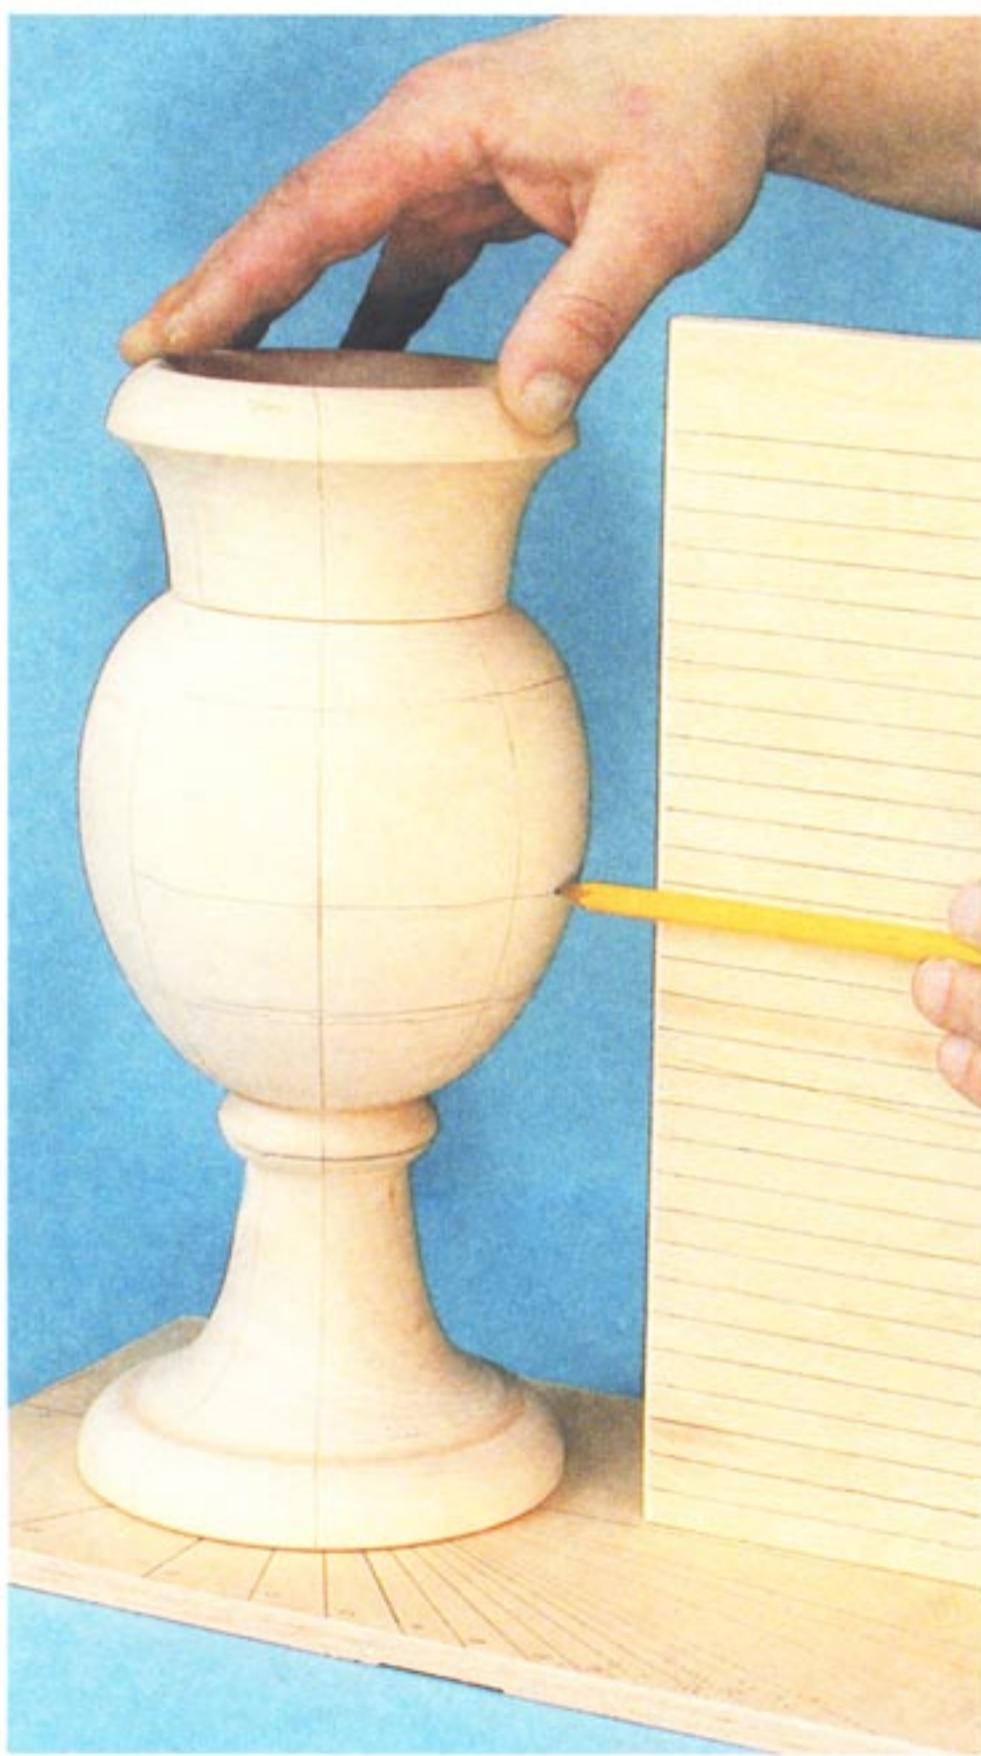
Нанесение шага на заготовку при помощи приспособления для разметки
